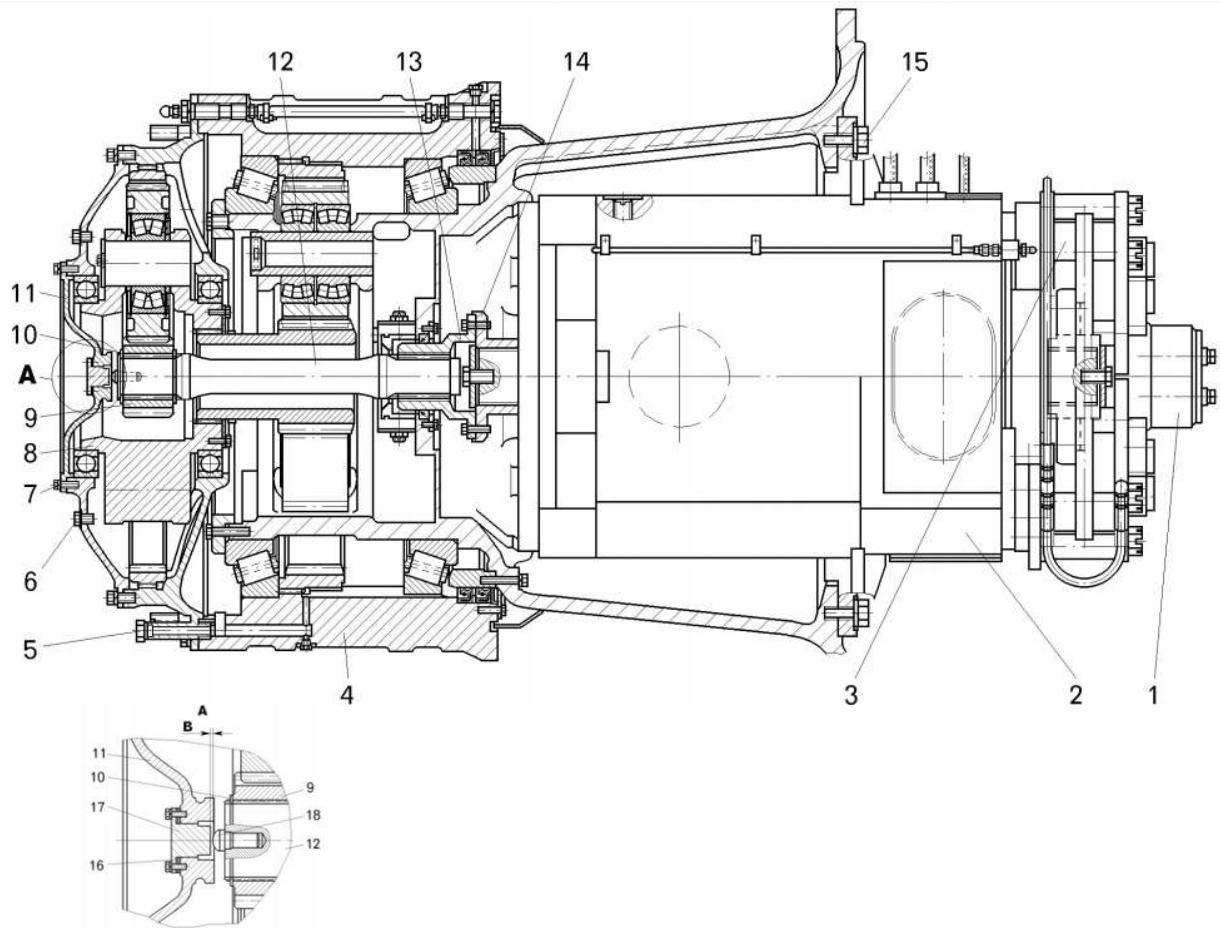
Электромотор-колесо: 1 – стояночный тормозной механизм; 2 – тяговый электродвигатель; 3 – рабочая тормозная система; 4 – ступица заднего колеса; 5 – щуп; 6 – пробка заливного отверстия; 7, 15 – болты; 8 – редуктор электромотор-колеса; 9 – солнечная шестерня первого ряда; 10 – стопорное кольцо; 11 – крышка; 12 – торсионный вал; 13 – фланец торсионного вала; 14 – фланец тягового электродвигателя; 16 – регулировочные шайбы; 17 – упор; 18 – упор сферический В – зазор
